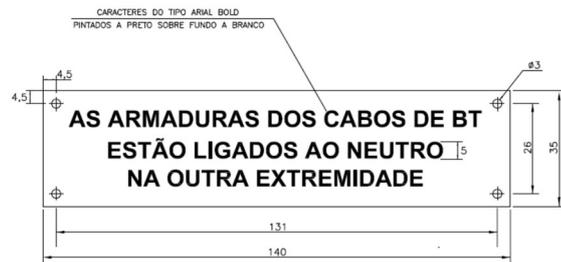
PT tipo CB • Aviso com a indicação do local de ligação das armaduras ao neutro
